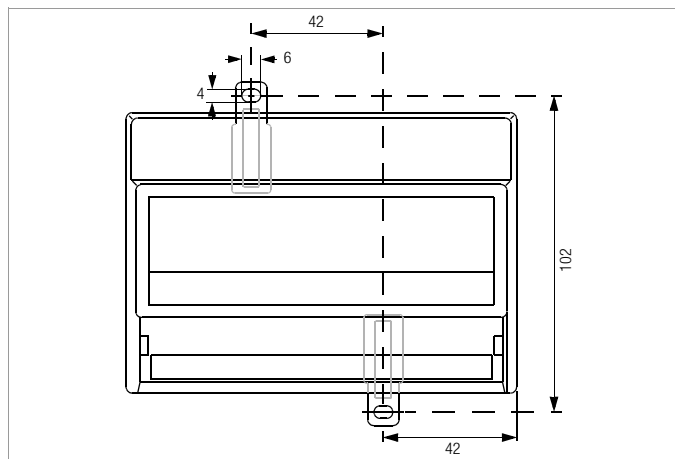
Maßzeichnung für Wandmontage (Frontansicht)
